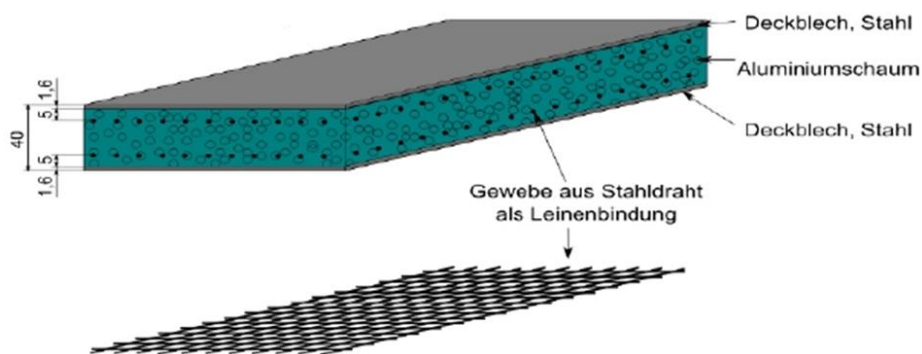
Konzept Stahl-Aluminiumschaum-Sandwichelement mit Stahldraht-Leinenbindung
